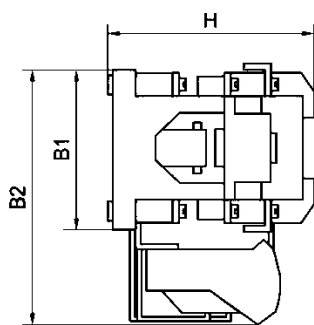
Пускатель реверсивный ПМЕ-200. Степень защиты - IP00
